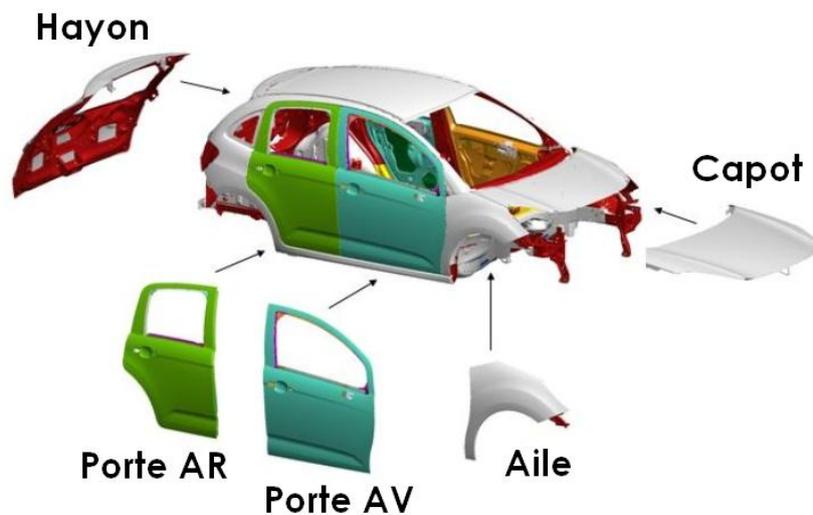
Assemblage des ouvrants dans la ligne de montage T35
